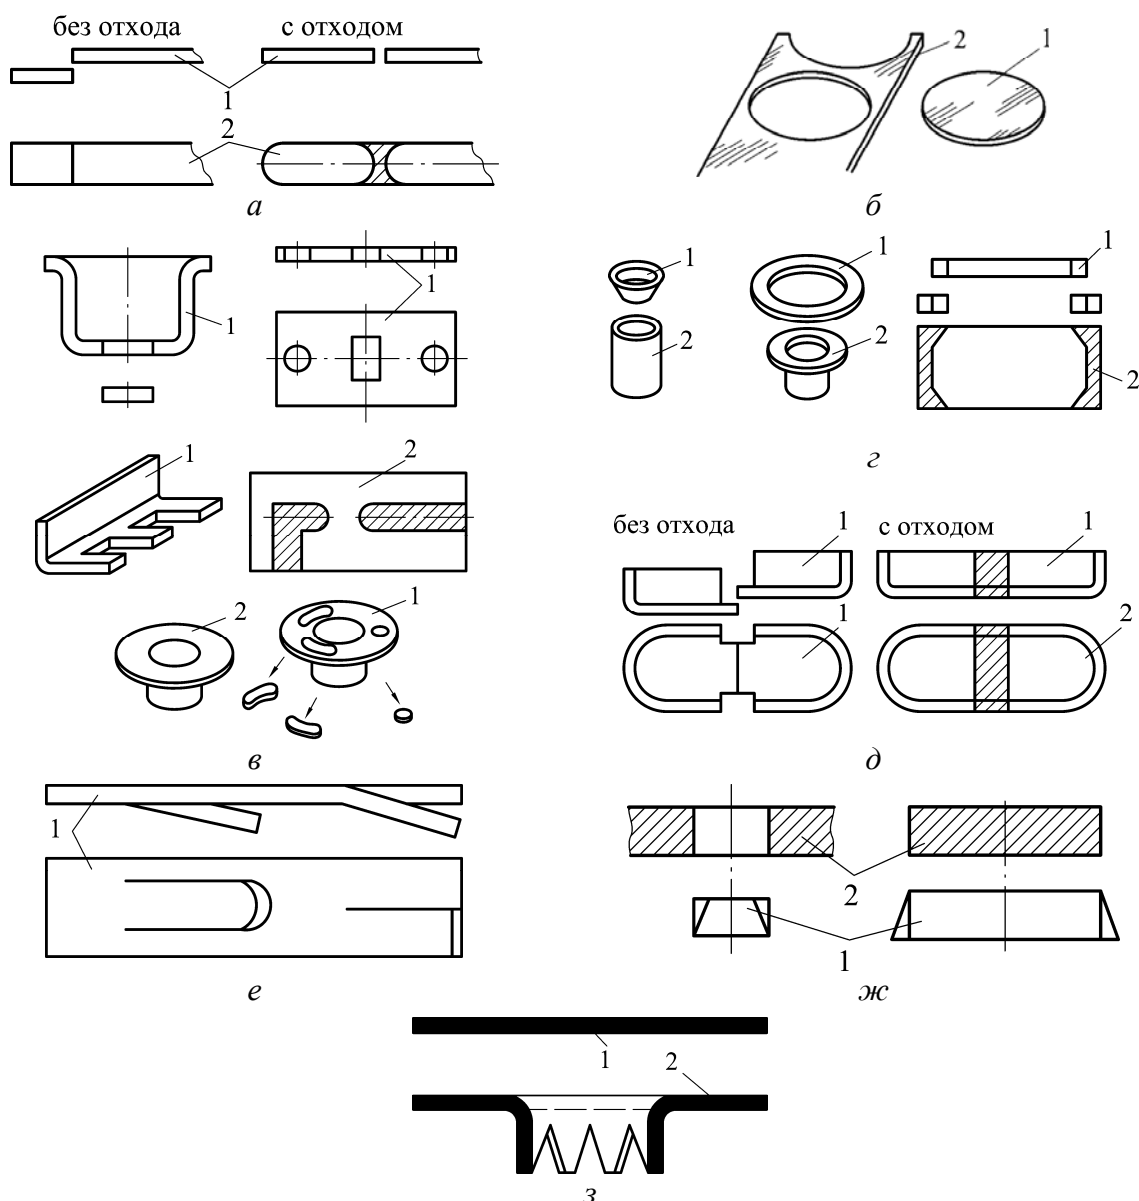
Деталь (1) и исходная заготовка (2), полученная разделительной операцией ей листовой штамповки: а – отрезкой; б – вырубкой; в – пробивкой; г – обрезкой; д – разрезкой; е – надрезкой; ж – зачисткой; з – проколкой
